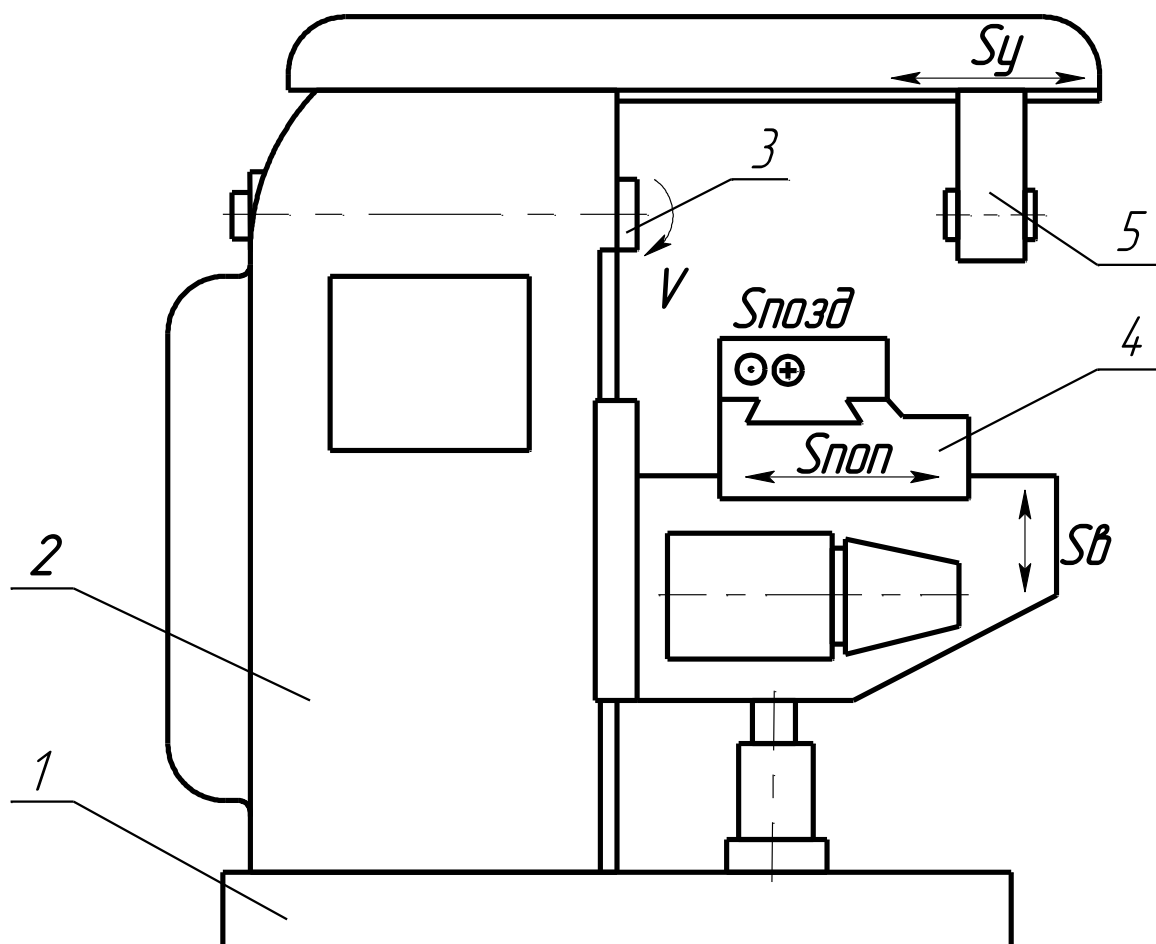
Загальний вигляд горизонтально-фрезерного верстата
